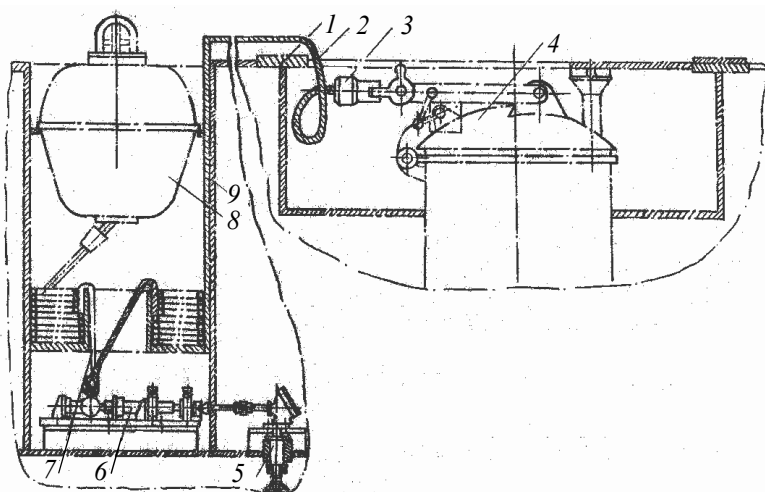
Устройство для выноса ходового троса с помощью аварийно-спасательного буя, расположенного в легком корпусе ПЛ (продольный разрез):
